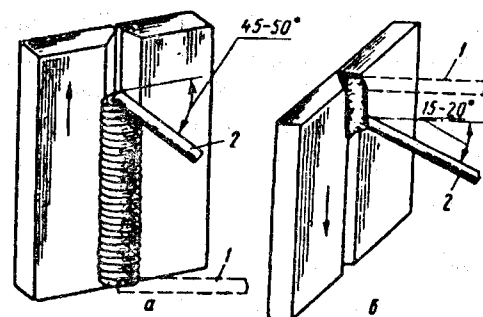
Сварка вертикальных швов: а — снизу вверх; б — сверху вниз; 1 — положение электрода в начале сварки; 2 — положение электрода в процессе наложения шва
